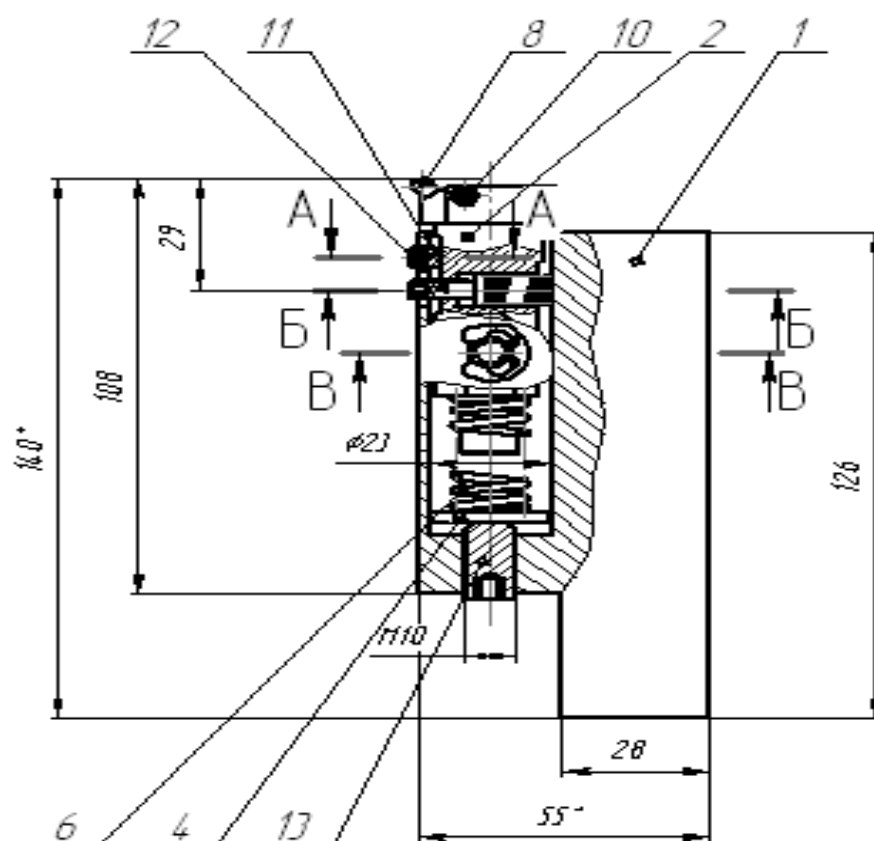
Конструкция приспособления для упрочняющей обработки шеек коленчатого вала
